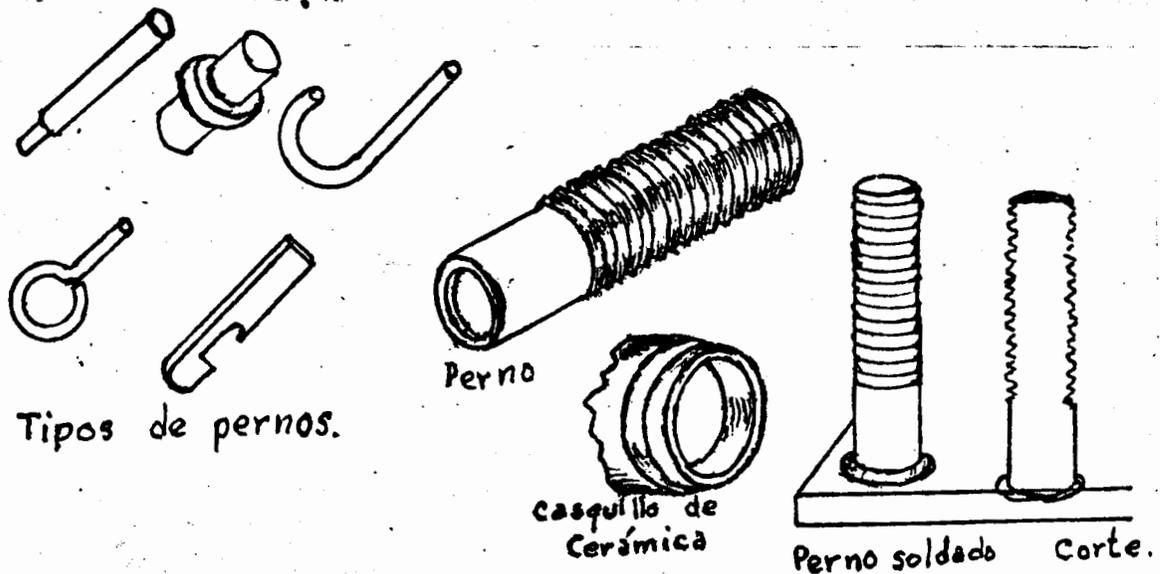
SOLDADO DE PERNOS MEDIANTE SOLDADURA DE ARCO.
